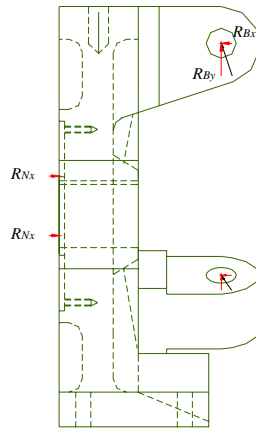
Distribución de las fuerzas en el soporte del indentador
